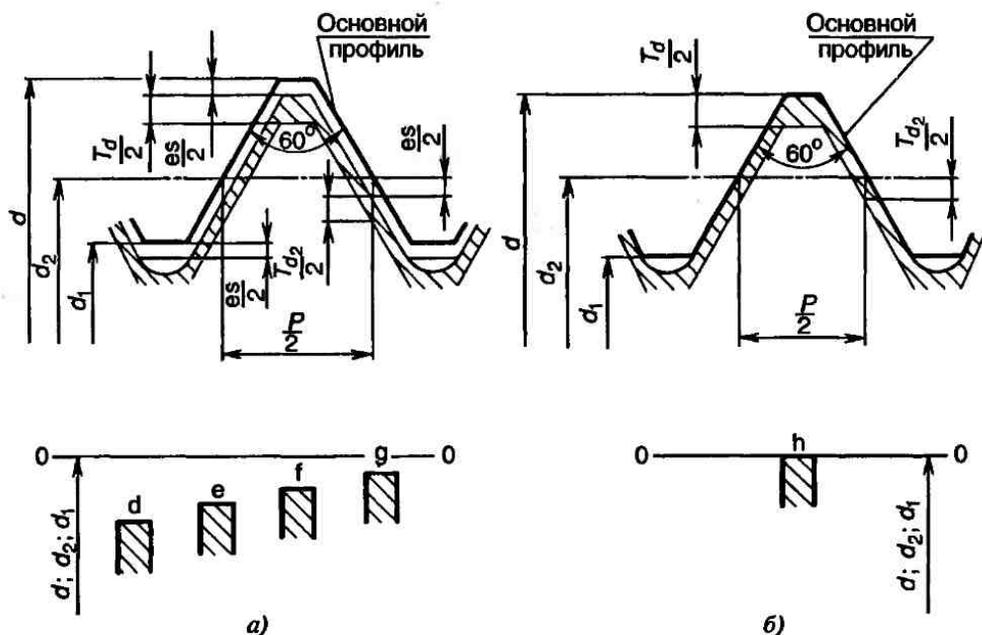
Положения полей допусков наружной резьбы:
